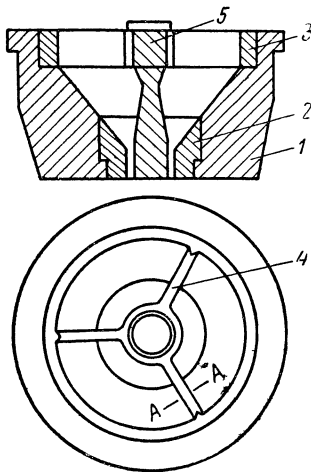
Схема мундштука для протяжки трубчатых заготовок.
